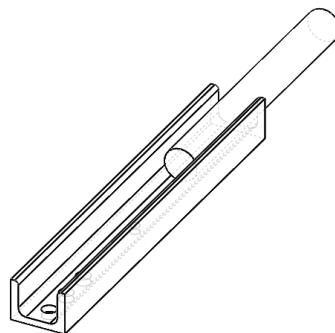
Barra de suporte (Anexo A1 - P.1.8).
